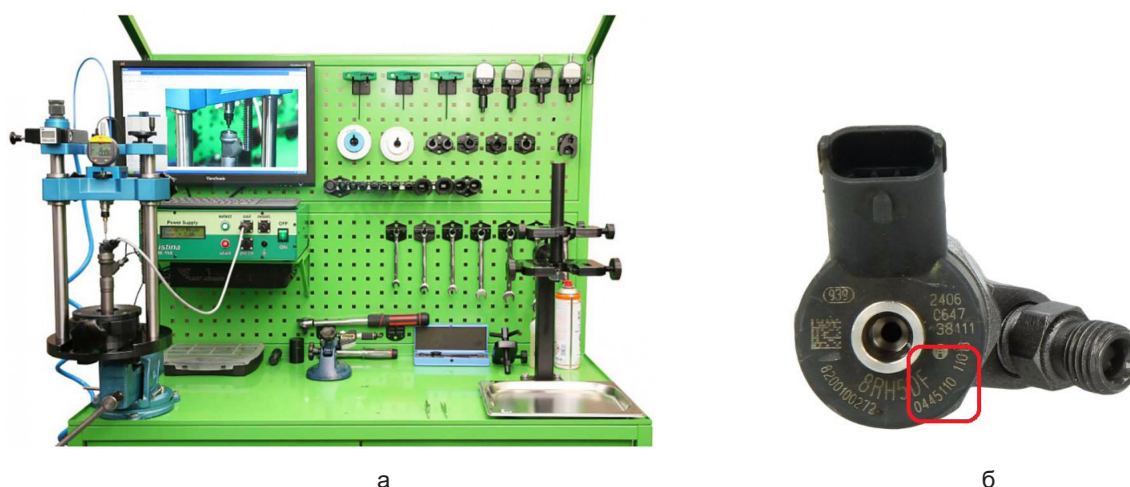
Стенд для регулировки и кодировки (калибровки) форсунок: а – Common Rail; б – верхняя часть форсунки с заводским номером 0 445 110 110
